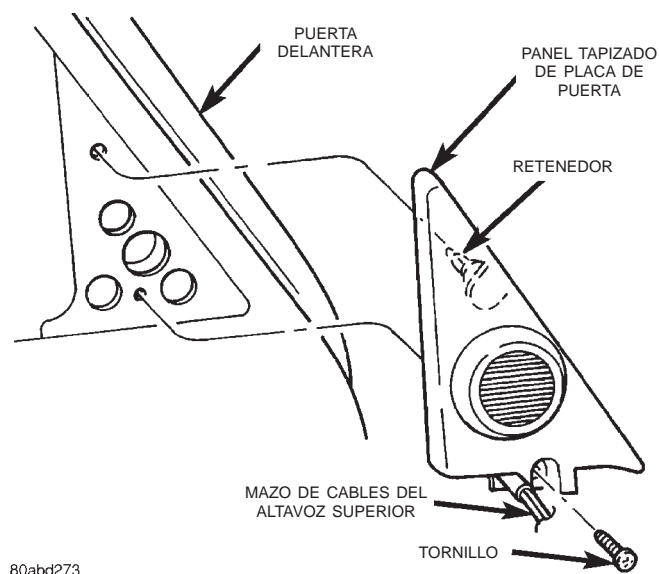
Desmontaje e instalación del panel tapizado de placa de puerta delantera
